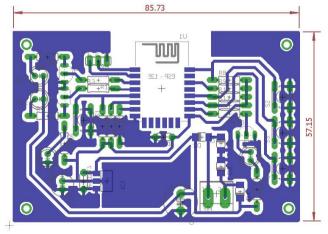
Diseño del PCB del segundo tipo de prototipos.
